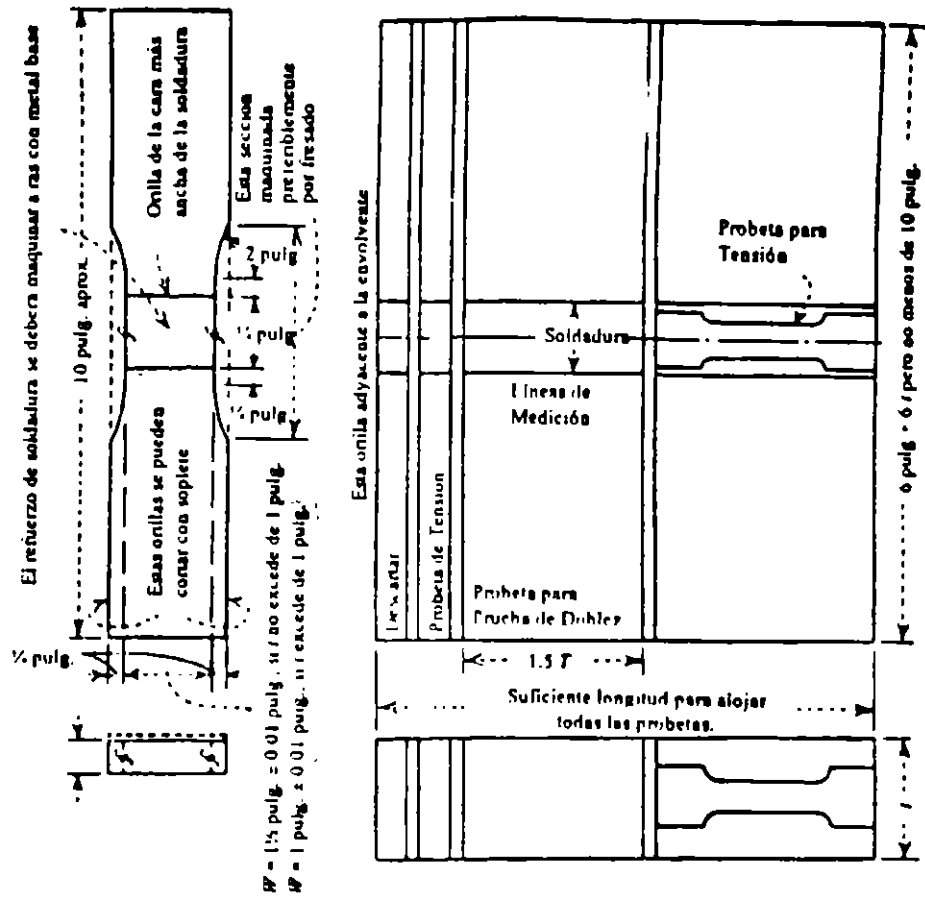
PROBETAS DE PRUEBA PARA PLACAS SOLDADAS LONGITUDINAMENTE
